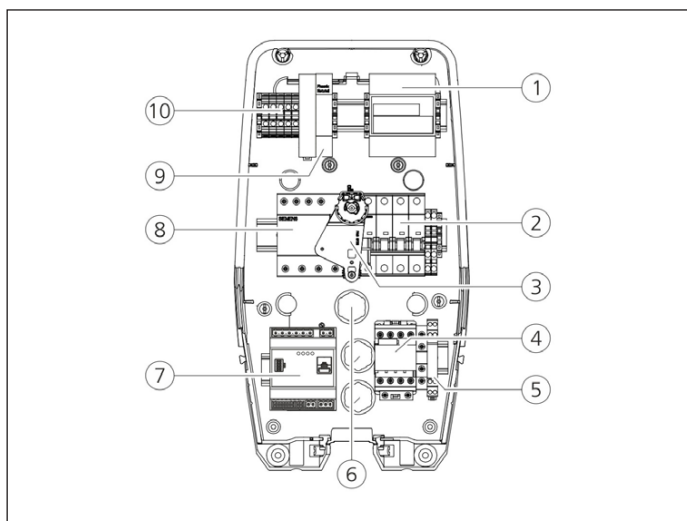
Внутренний вид Нижняя часть корпуса (пример)
